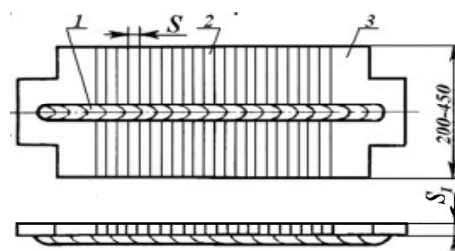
Пластина з наплавленням: 1 – валик; 2 – брусок; 3 – планка приставна.
